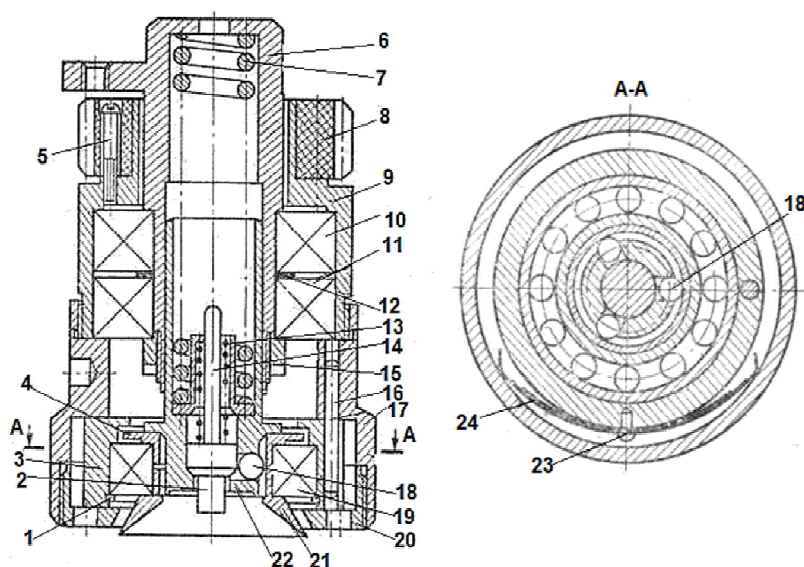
Обкочувальний патрон машини ВУВ: 1, 12 - кільця; 2 - щуп; 3 - обойма 10, 11, 19 - підшипники; 15, 20 - вкладиші; 16 - вісь; 17 - корпус нижній; 18 - кулька; 21 - центратор; 22 - шток; 23 - заклепка; 24 - ресора пружина.
